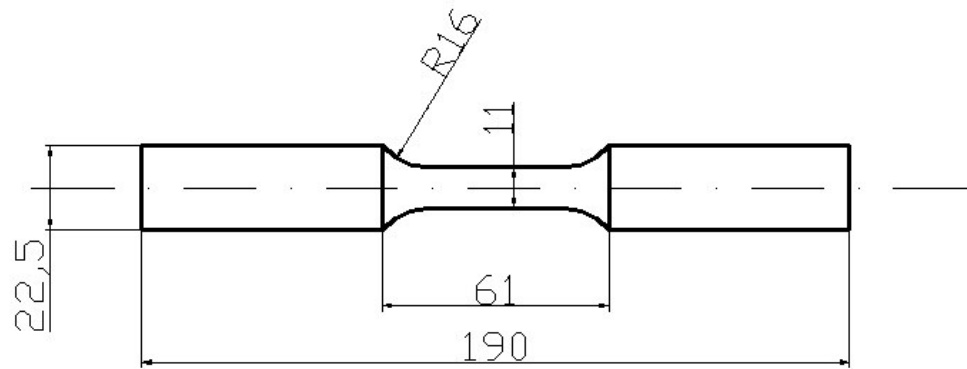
Desenho com as dimensões do corpo-de-prova após a usinagem.
